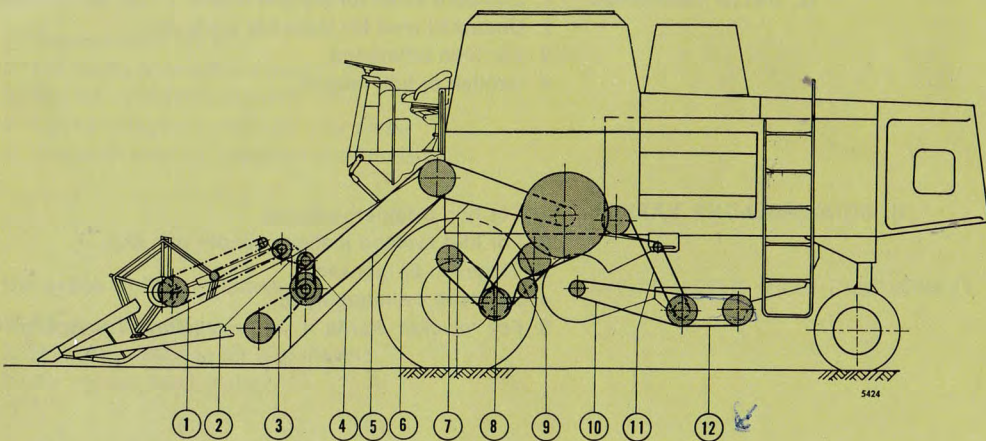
Remdrift för skördetröska i tankutförande (vänster sida).
